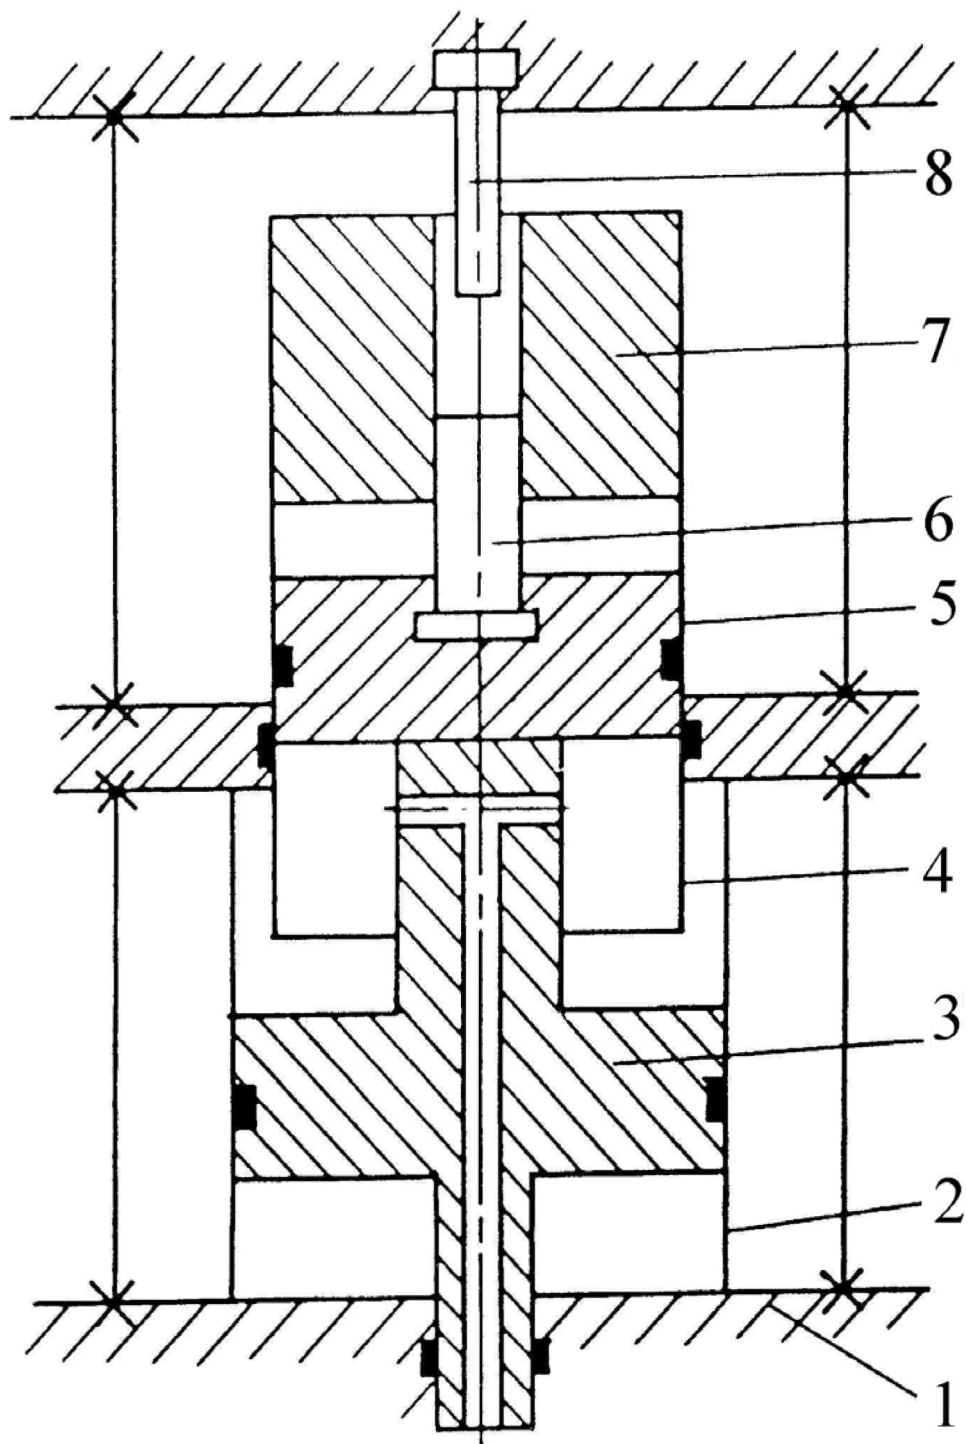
Конструкция особомалогобаритного пресса для выдавливания с активными силами трения
